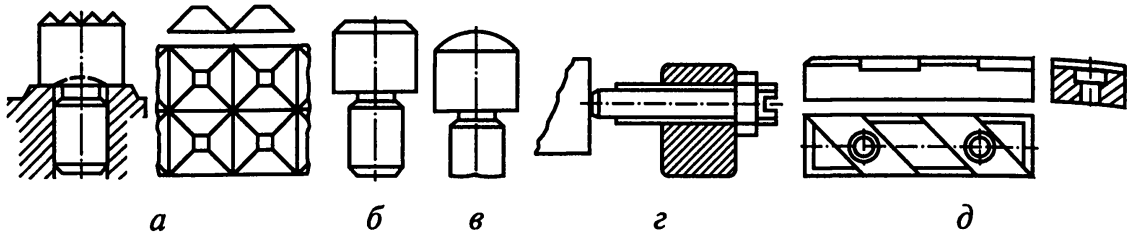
Опоры для установки на плоские поверхности: *а* — с рифленой головкой; *б* — с плоской головкой; *в* — со сферической головкой; *г* — регулируемые опоры; *д* — опорные пластины
